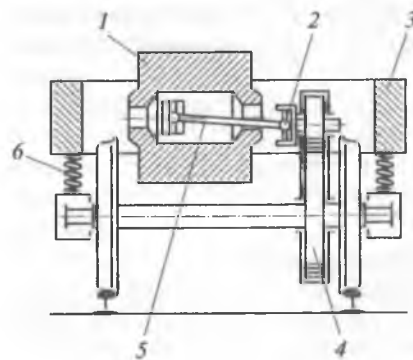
Схема передачи крутящего момента с торсионным валом:
